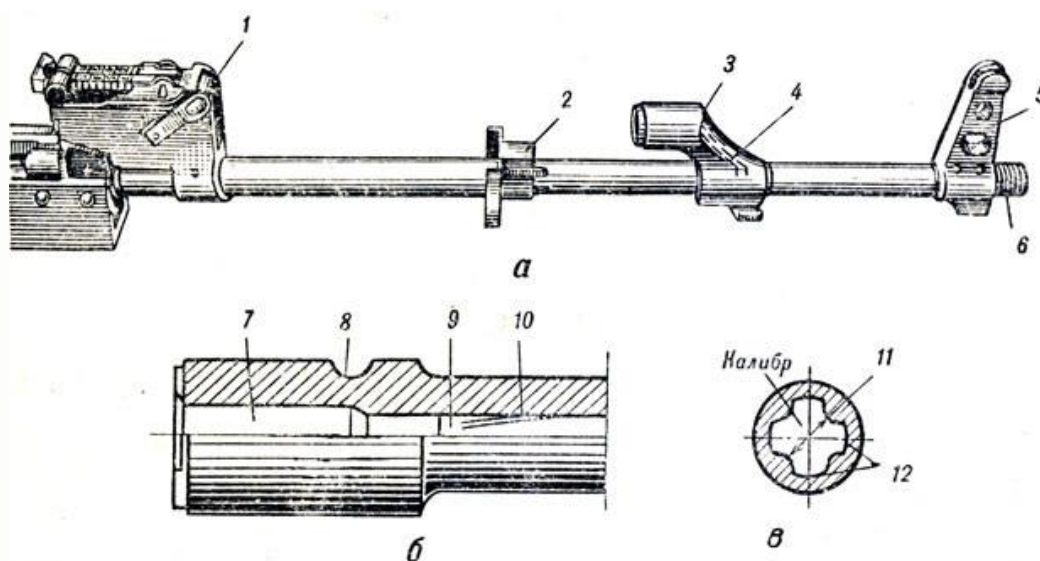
Ствол: *а* — общий вид; *б* — казенная часть в разрезе; *в* — сечение ствола; 1 — колодка прицела; 2 — соединительная муфта; 3 — газовая камера; 4 — газоотводное отверстие; 5 — основание мушки; 6 — резьба; 7 — патронник; 8 — выем для шпильки ствола; 9 — пульный вход; 10 — нарезная часть; 11 — поле; 12 — нарезы
